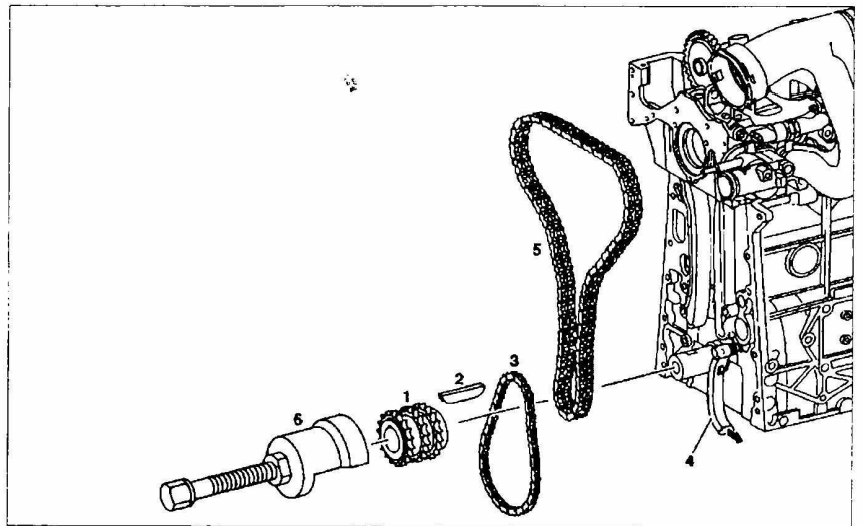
Снятие и установка зубчатого шкива коленчатого вала:
